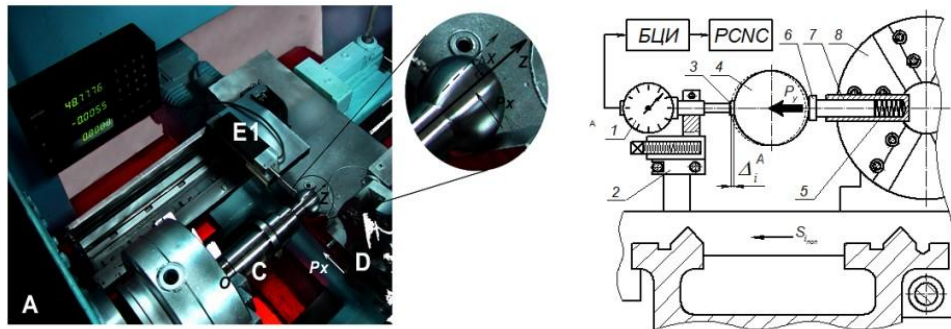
Схема нагружения и деформирования детали при использовании нагрузочного устройства: 1 — индикатор перемещений; 2 — каретка диагностического модуля; 3 — измерительный стержень; 4 — элемент детали; 5 — пружина; 6 — нажимной элемент; 7 — нагрузочное устройство; 8 — инструментальная головка станка
